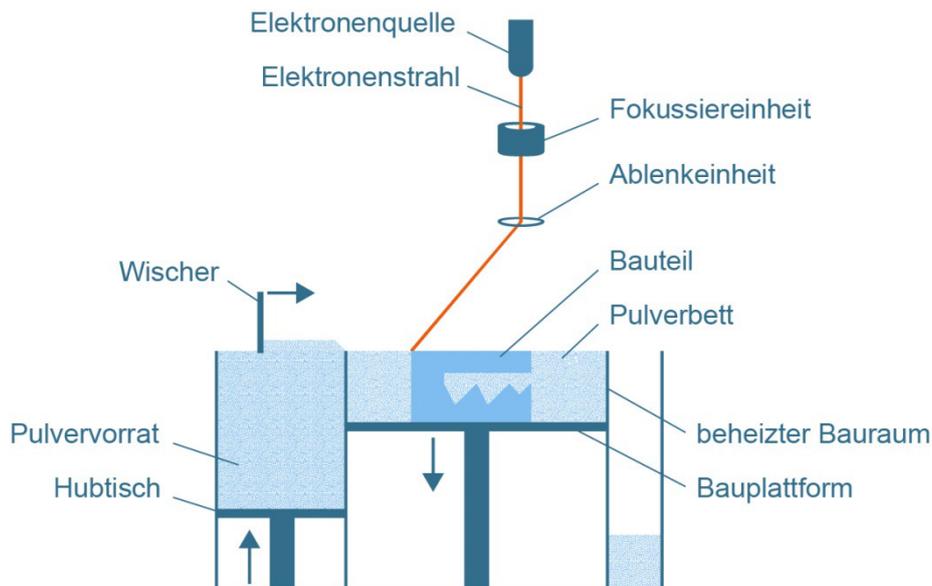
Aufbau und Elemente einer Elektronenstrahlschmelz-Anlage
